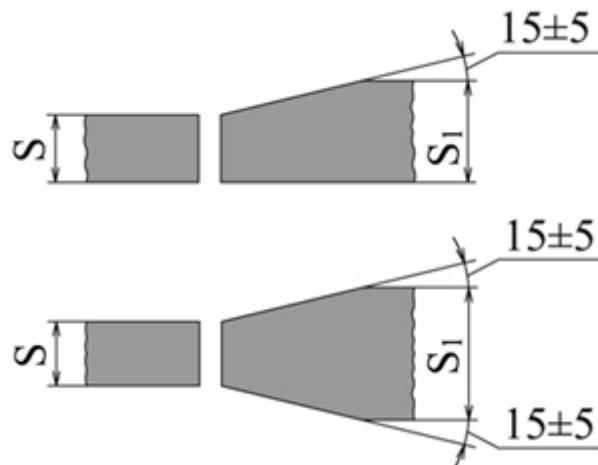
Подготовка разнотолщинных деталей к сварке
